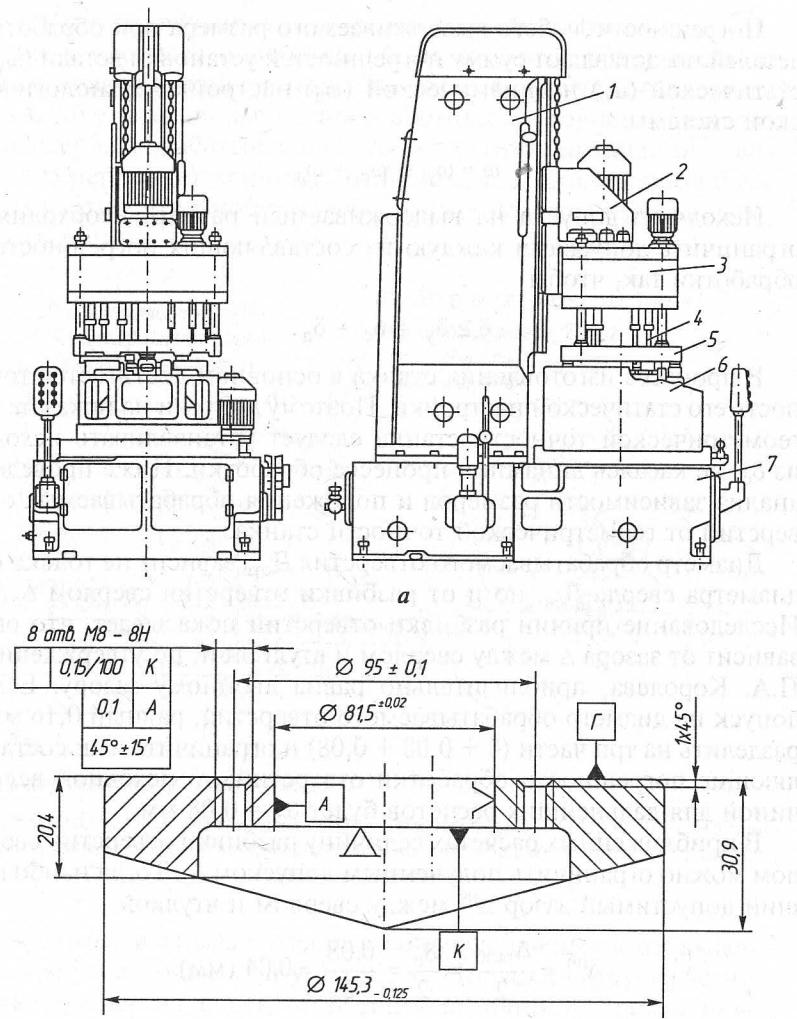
24-шпиндельный вертикальный сверлильно-резьбонарезной агрегатный станок:
